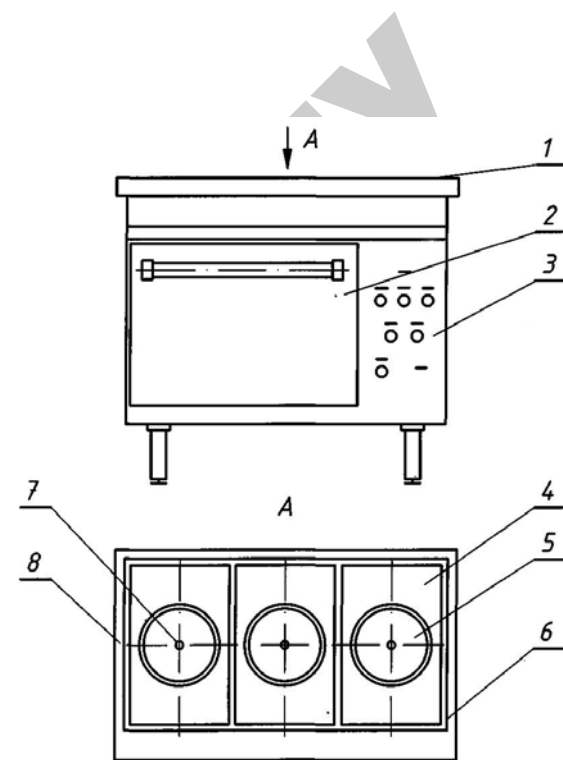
Схема составного плитного настила: 1 – рабочая поверхность плиты; 2 – дверца парожарочного шкафа; 3 – пульт управления; 4 – конфорка; 5 – центральный вкладыш; 6 – облицовочная поверхность; 7 – центральное отверстие; 8 – тепловые зазоры
